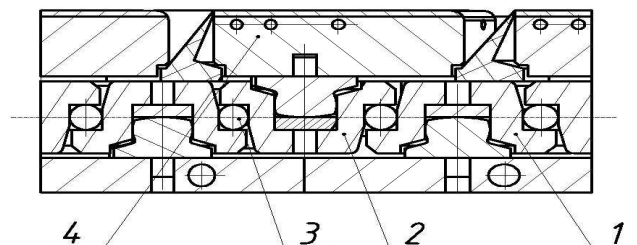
Подшипник опорно-упорный ПДУ-120/260 модернизированной турбины 103ТТ.
